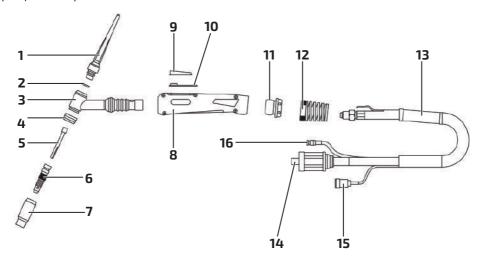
Горелка для аргонодуговой сварки воздушного охлаждения.
